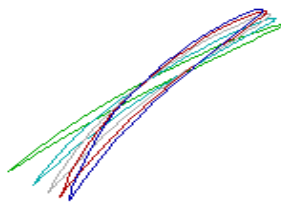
Профили рабочего колеса компрессора в пяти сечениях
